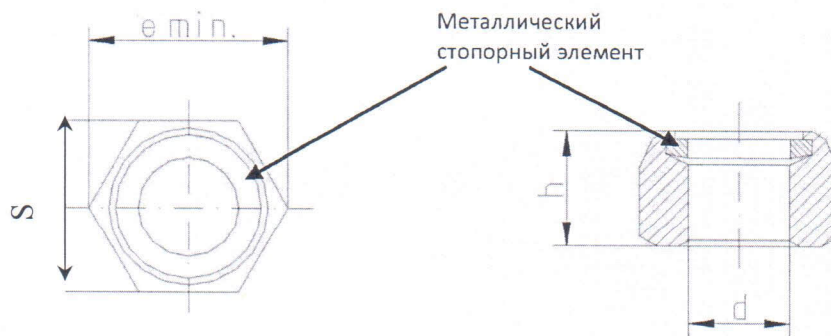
Конструкция и обозначение геометрических размеров FS-гайки
